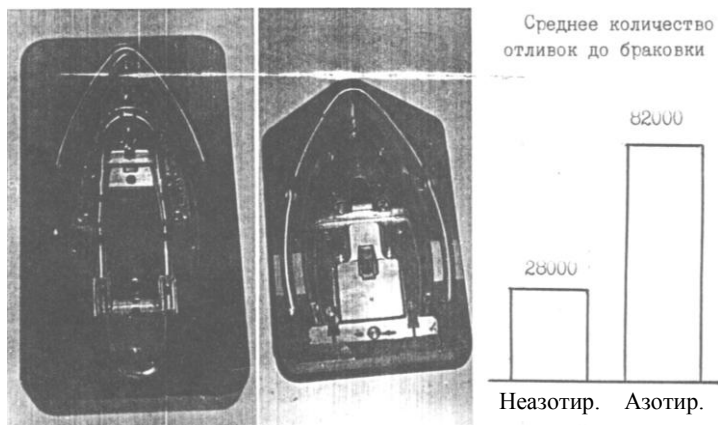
Лит-формы для изготовления корпуса утюга из алюминия
